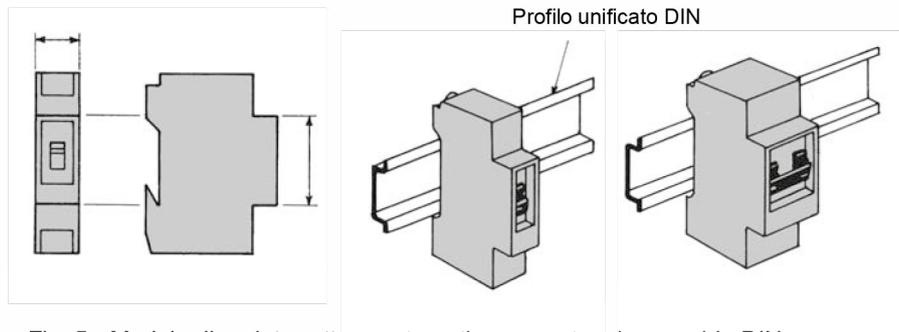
Modulo di un interruttore automatico e montaggio su guida DIN.
